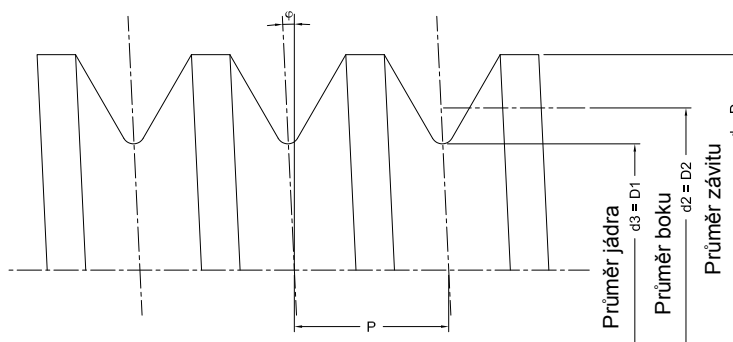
Pravý závit se šroubem stroje otáčejícím se doprava
